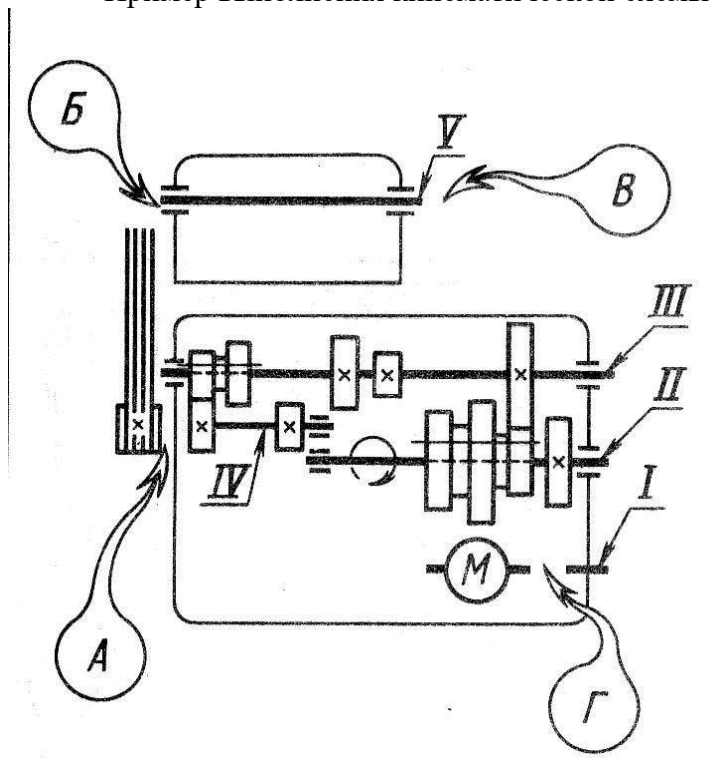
Незаконченная кинематическая схема бабки токарно-винторезного станка мод. 1616
